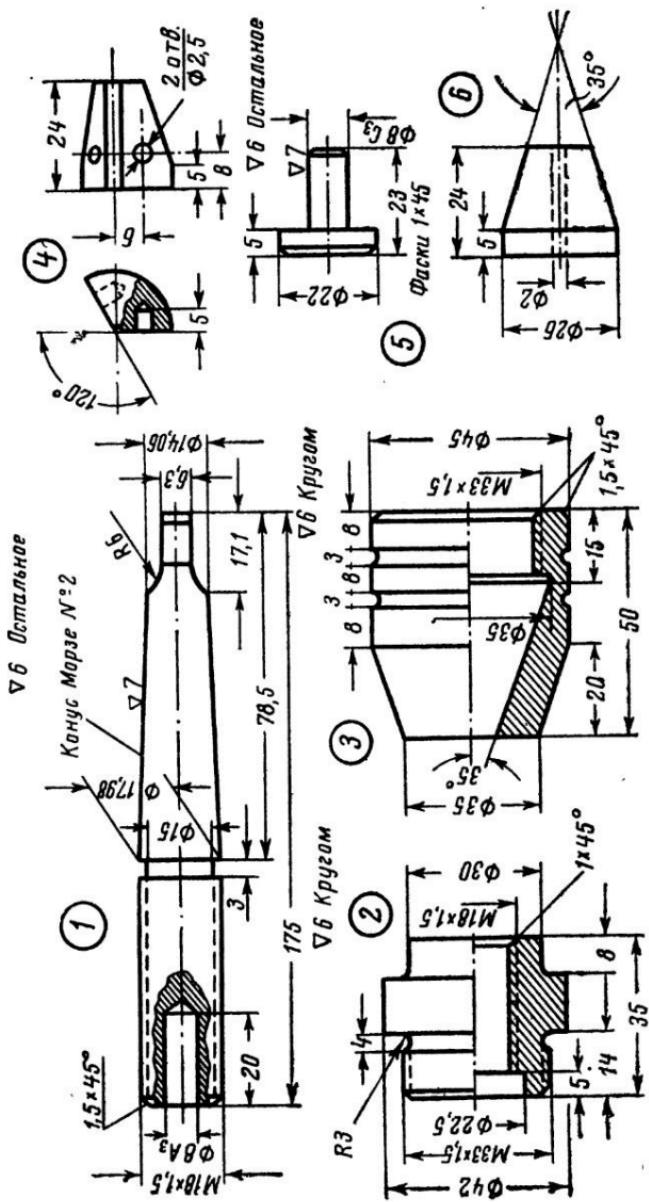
Детали сверлильного патрона: 1 — хвостовик; 2 — втулка; 3 — корпус; 4 — кулачок;
